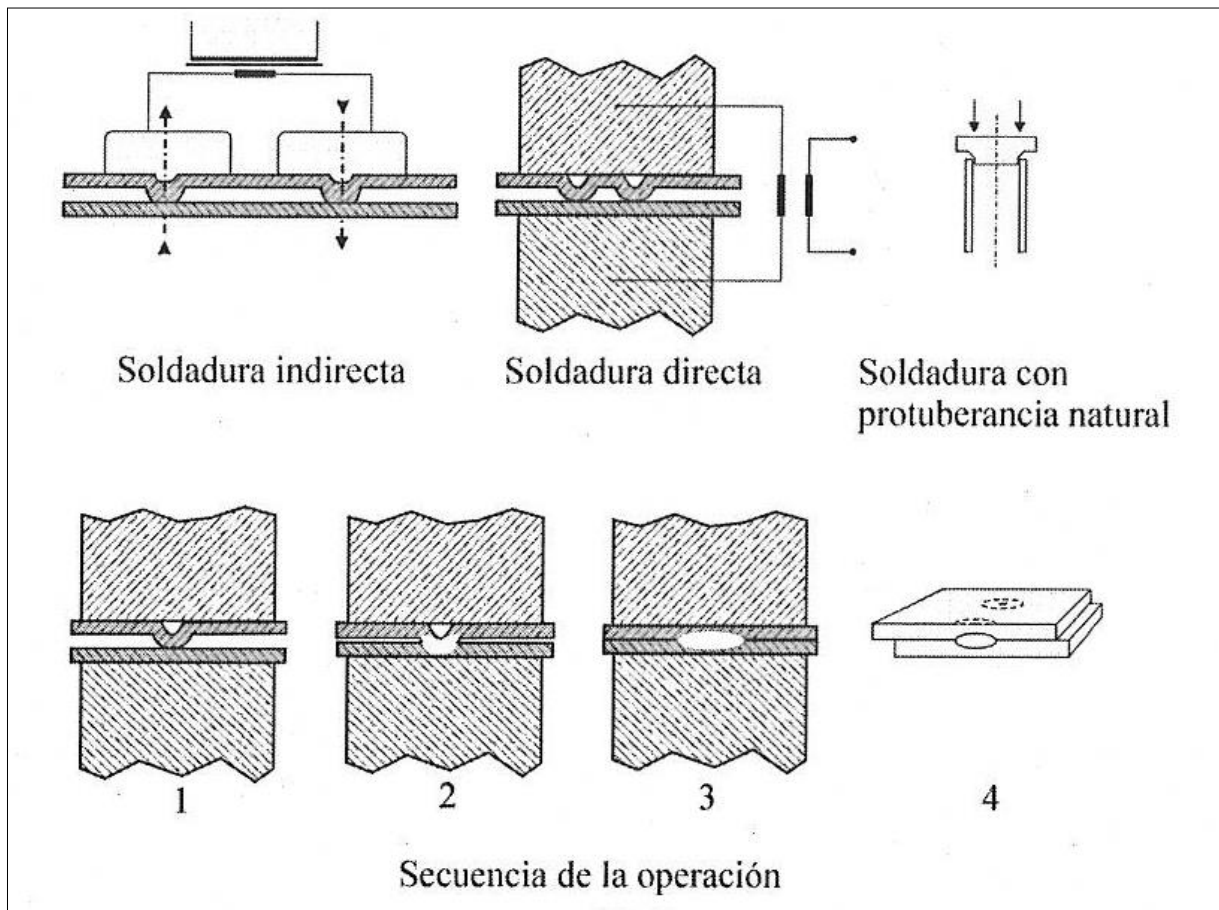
Diferentes casos de soldadura por proyección.
